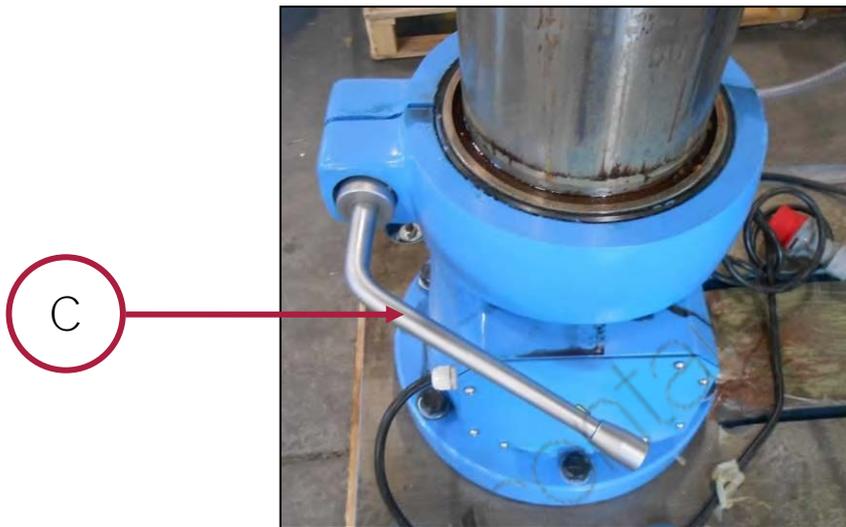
Leva di bloccaggio dello scorrimento angolare della colonna.
